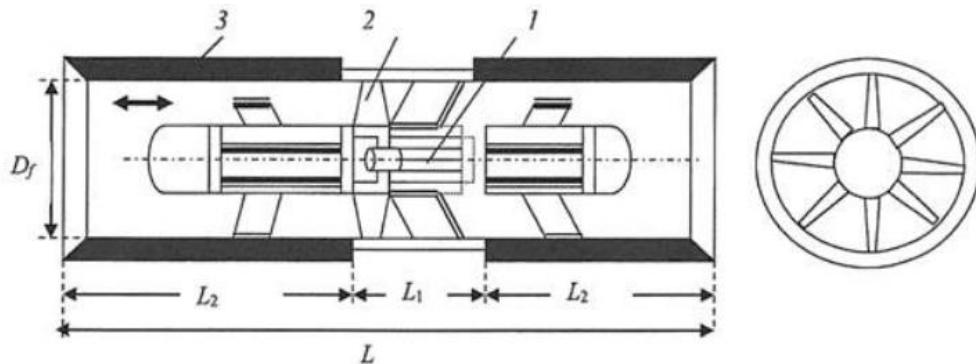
Конструктивная схема реверсивного струйного вентилятора
